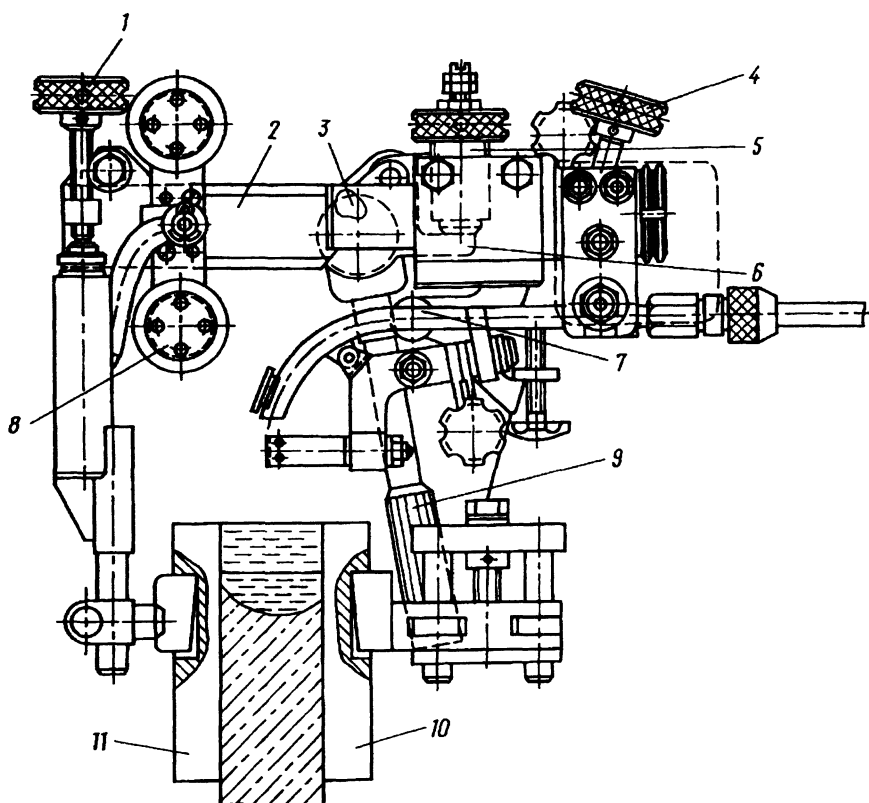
Сварочная головка полуавтомата А671Р
